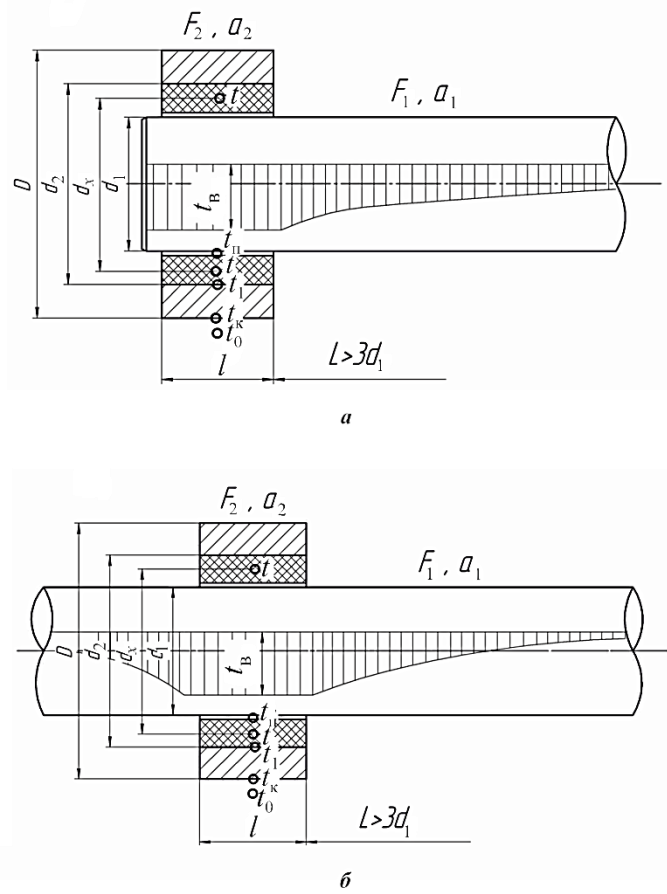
Схема подшипникового узла с применением наполненного полимера: *a* – концевой подшипник; *б* – срединный подшипник; d_1 – диаметр вала в зоне трения; d_2 – наружный диаметр подшипника; D – наружный диаметр корпуса подшипника; l – длина подшипника; L_1 и L_2 – длина вала с интенсивным теплообменом в левую и правую сторону от подшипника соответственно
